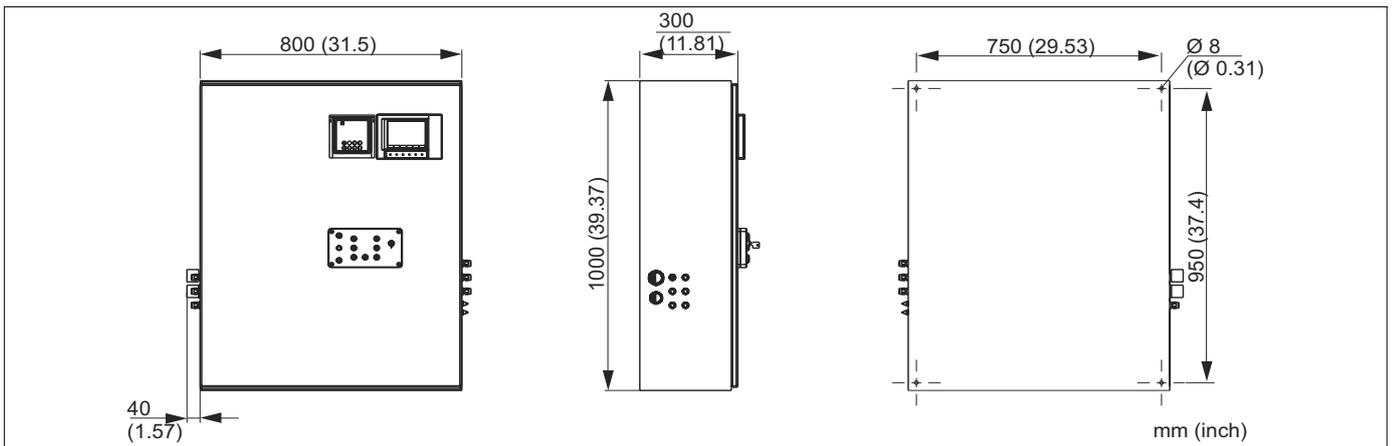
Dimensions du boîtier CYC310, version matière synthétique
